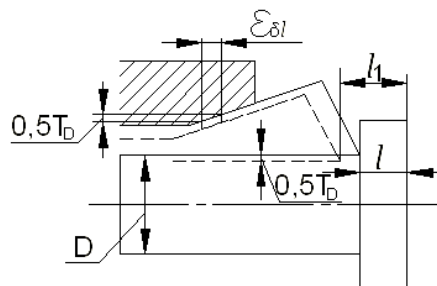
Схема виникнення похибки базування при закріпленні заготовки в патроні з цангою, що втягується.
